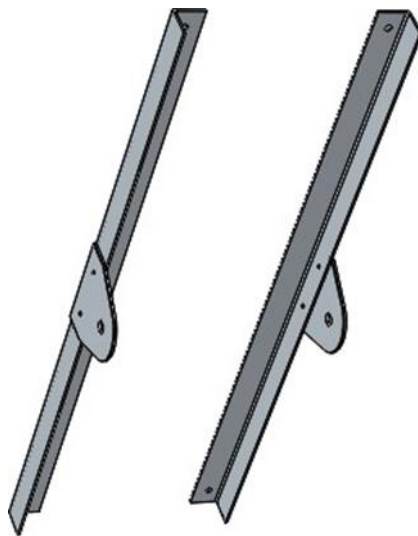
Загальний вигляд горизонтального – рухомого механізму
